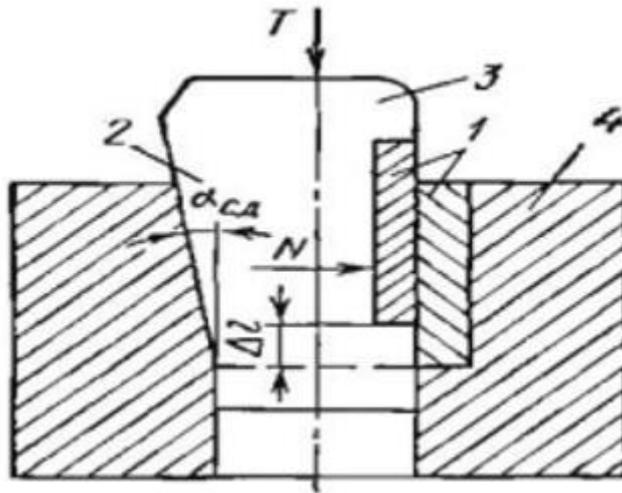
Схема холодной сварки сдвигом:
